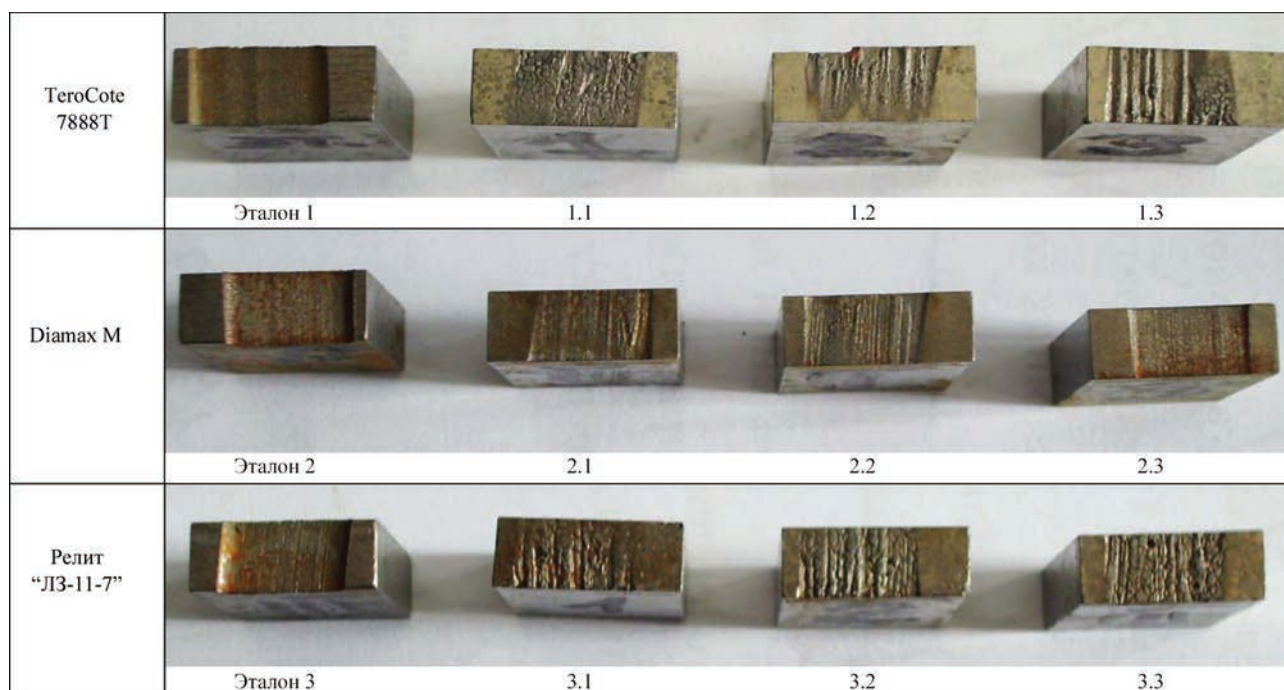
Внешний вид образцов, наплавленных различными композиционными материалами, после испытаний на гидроабразивный износ (путь трения — 250 м)
